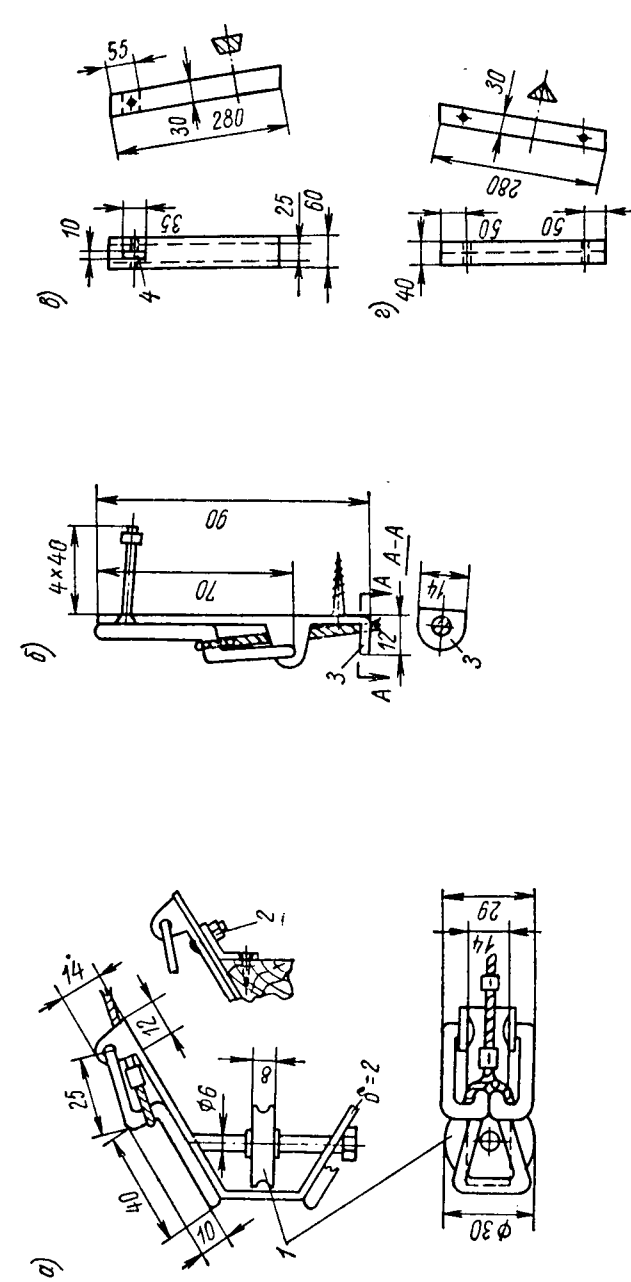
«Ладога» М1-Д: а — бортовые защелки (вид сверху и сборку) (вид сверху и сборку); б — кормовая защелка с направляющим кольцом; в — актерштейн; г — форштевень.
